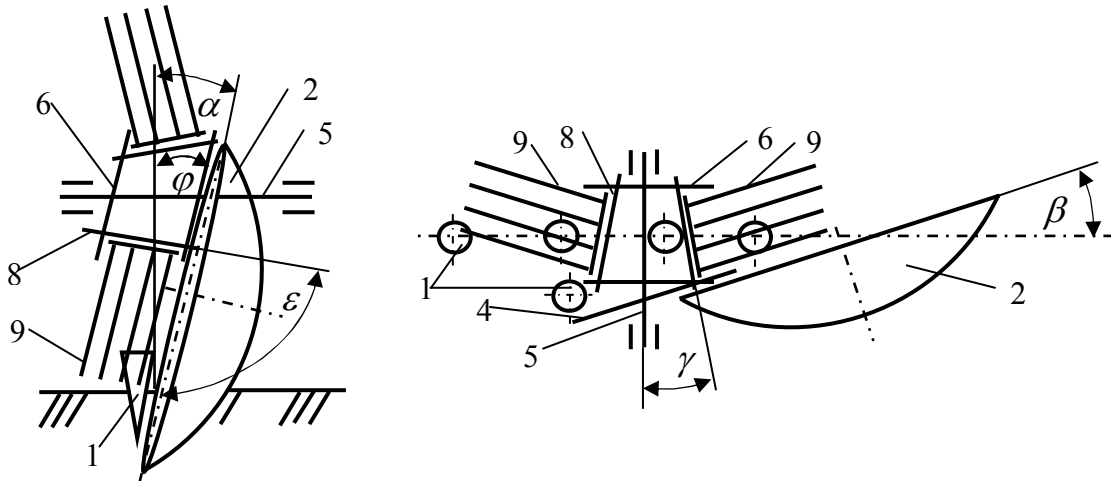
Конструктивна схема АВТКРО: а – вигляд спереду; б – вигляд зверху
